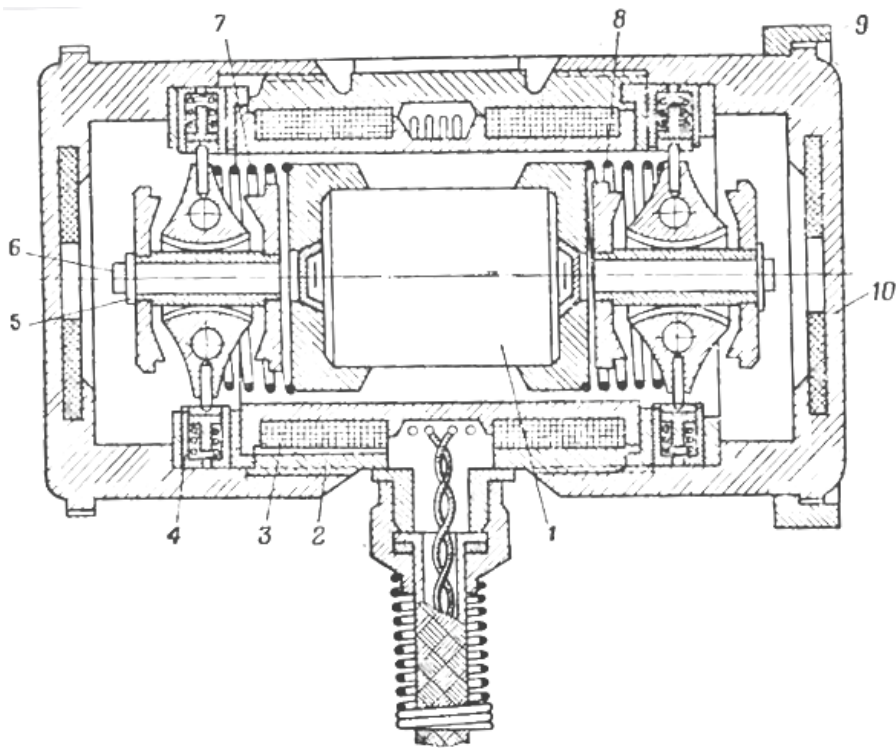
Конструкція датчика вібрації: 1 – збалансована маса; 2 – корпус датчика; 3 – котушка; 4 – підшипник; 5 – шайба; 6 – гвинт; 7, 8 – циліндричні пружини; 9 – фланець; 10 - кришка
